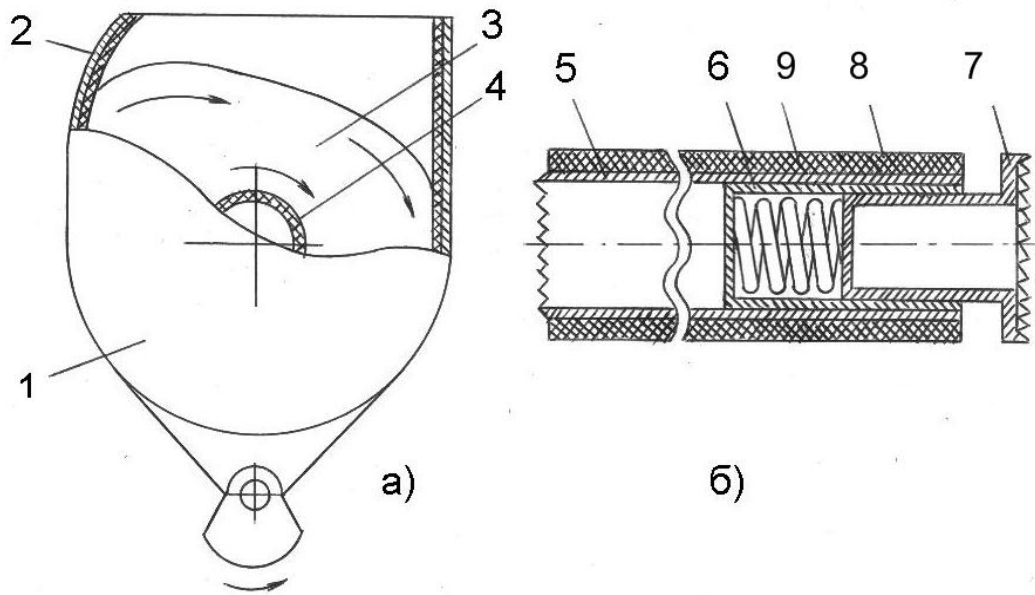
Схема модернизированной рабочей камеры (а) с цилиндрической вставкой (б)
